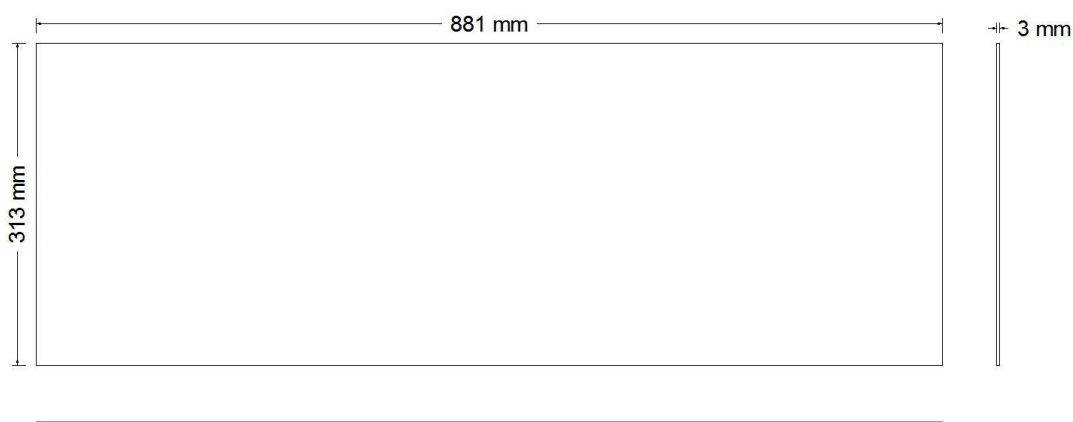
Vistas esquemáticas de um painel tipo M.
